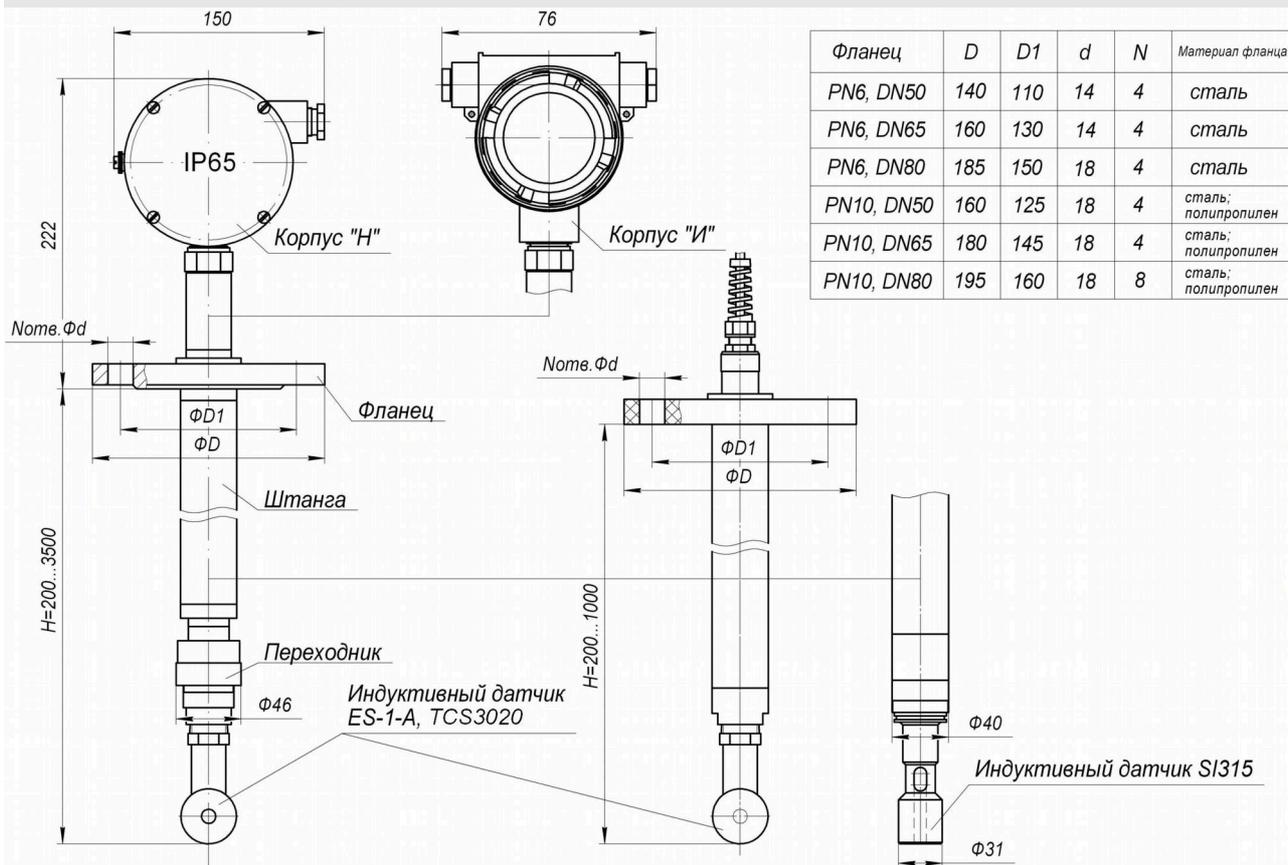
Габаритные и монтажные размеры первичного преобразователя с индуктивными датчиками ES-1-A, TCS3020, SI 315
